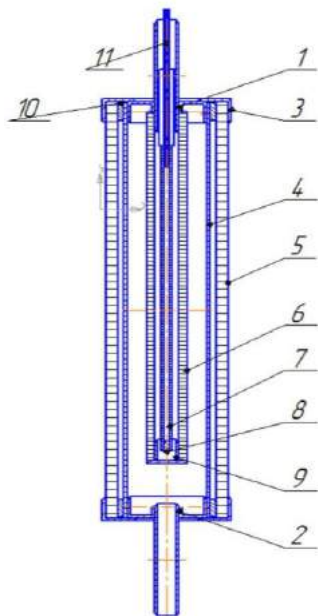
Устройство каталитического нагревательного элемента: 1-втулка с патрубком для подачи жидкого топлива; 2-втулка с газовым патрубком; 3-колпачок; 4-распределительный блок; 5-каталитический блок; 6-испарительный блок; 7-капиллярный блок; 8-заглушка капиллярного блока; 9-заглушка испарительного блока; 10-вставка дистанцирующая; 11-втулка капиллярного подвода жидкого топлива
